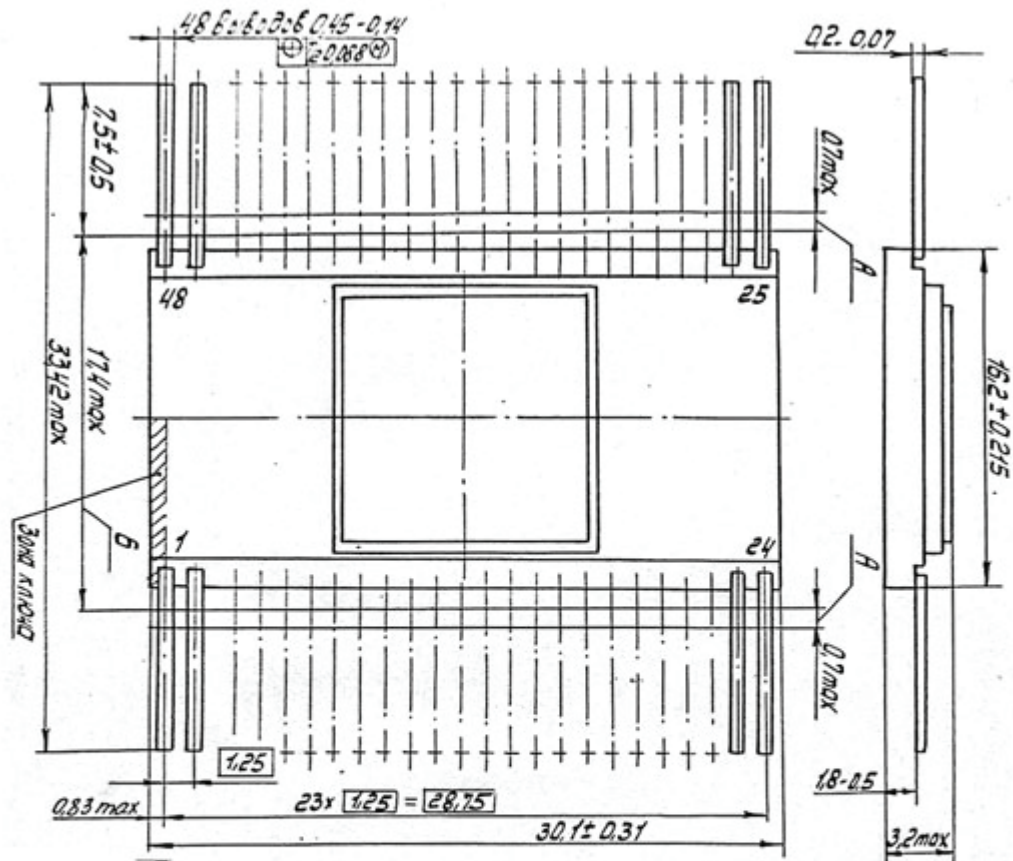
Габаритный чертеж корпуса N16.48-1B
